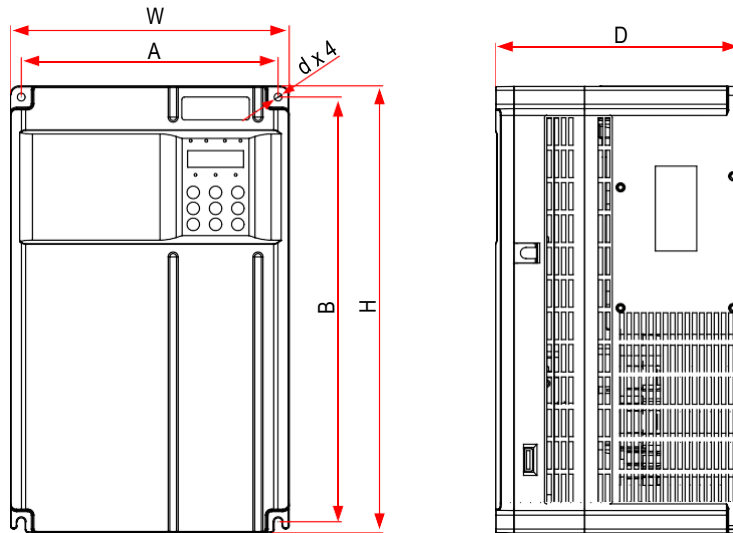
GT600-4T18.5G(B)~GT600-4T37G(B) 外型尺寸及安装尺寸示意图
